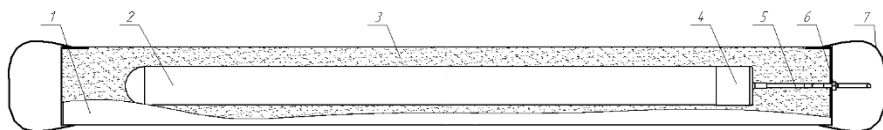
Схема конструкции АЗ.РСЗ.ФС.ПК
